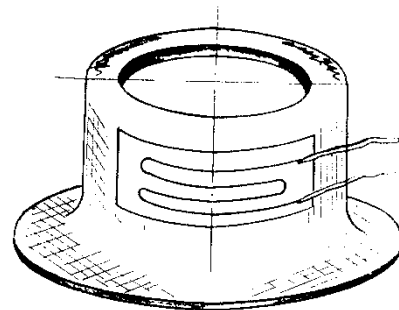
Схема наклеювання тензорезистора на корпус ФД
